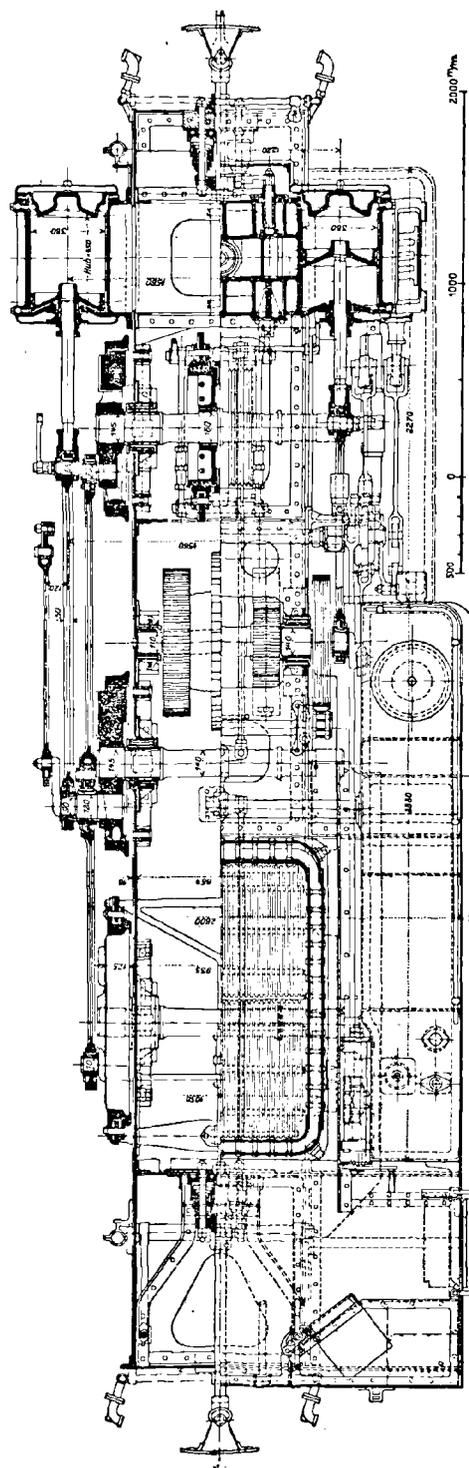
Machine du Brünig. — Plan et coupe horizontale.
